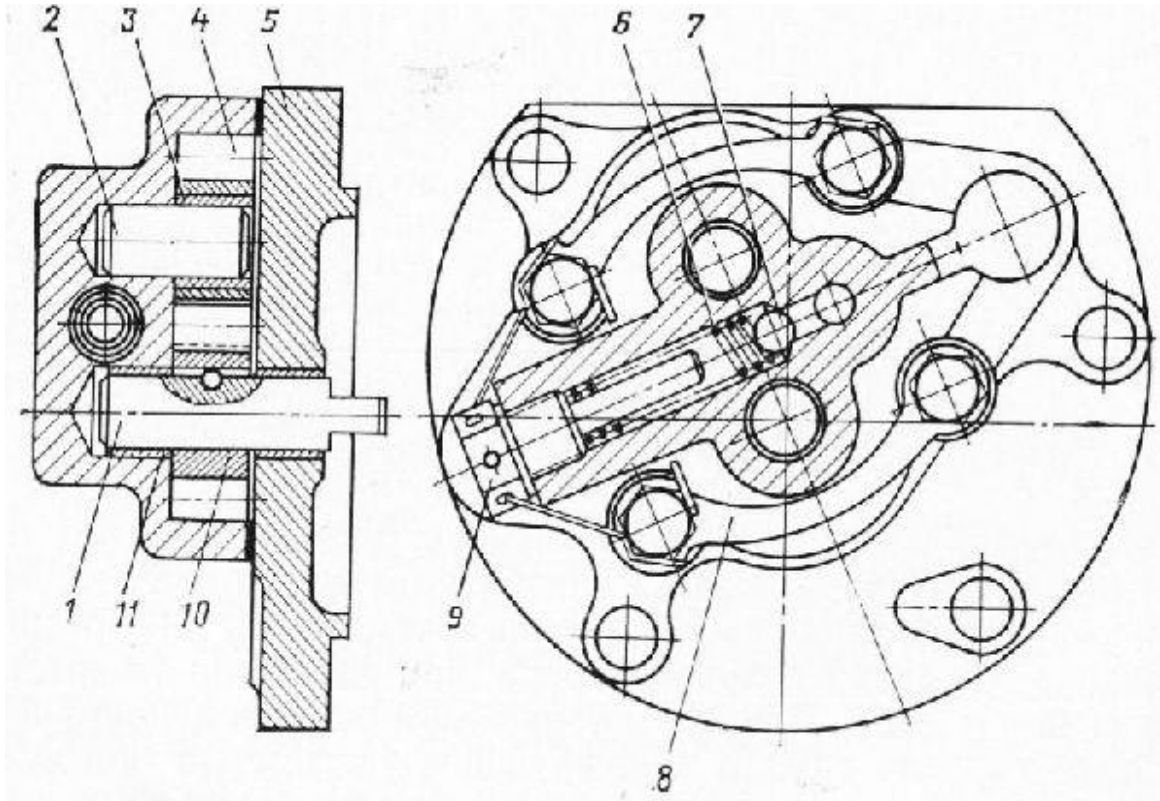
Насос коробки швидкостей масляний: 1 - валик; 2 - вісь; 3 - втулка; 4 - шестерня; 6 – пружина; 7 - кулька; 8 - планка; 9 - пробка; 10 - привідна шестерня; 11 – втулка.
